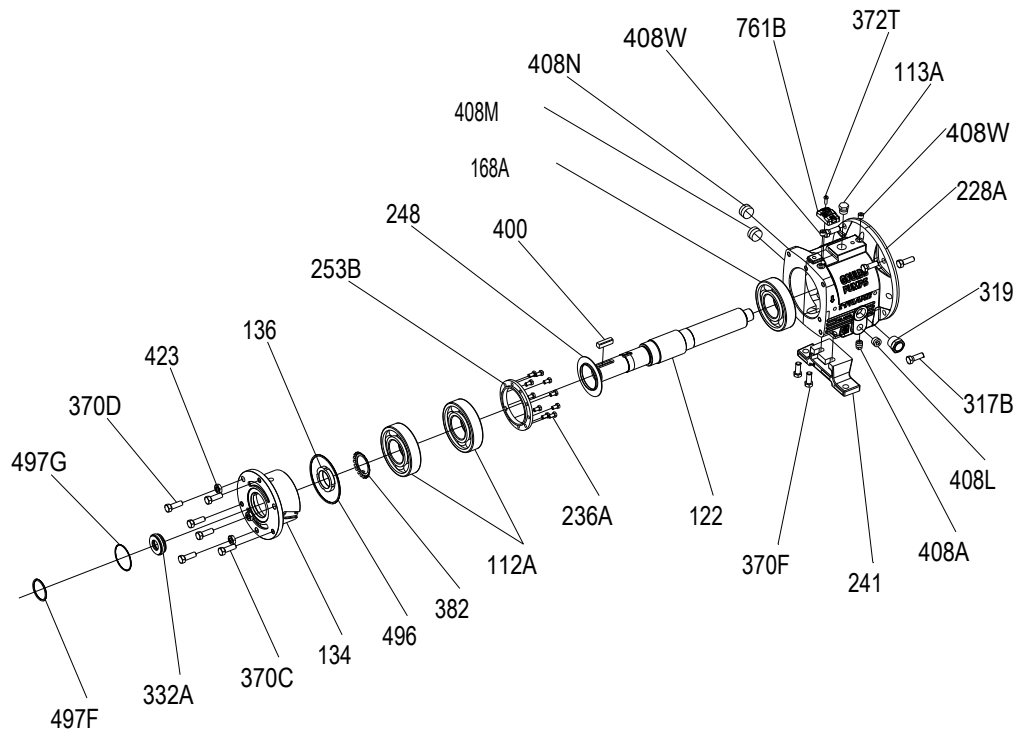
LTi-Stützschaale Explosionszeichnung
